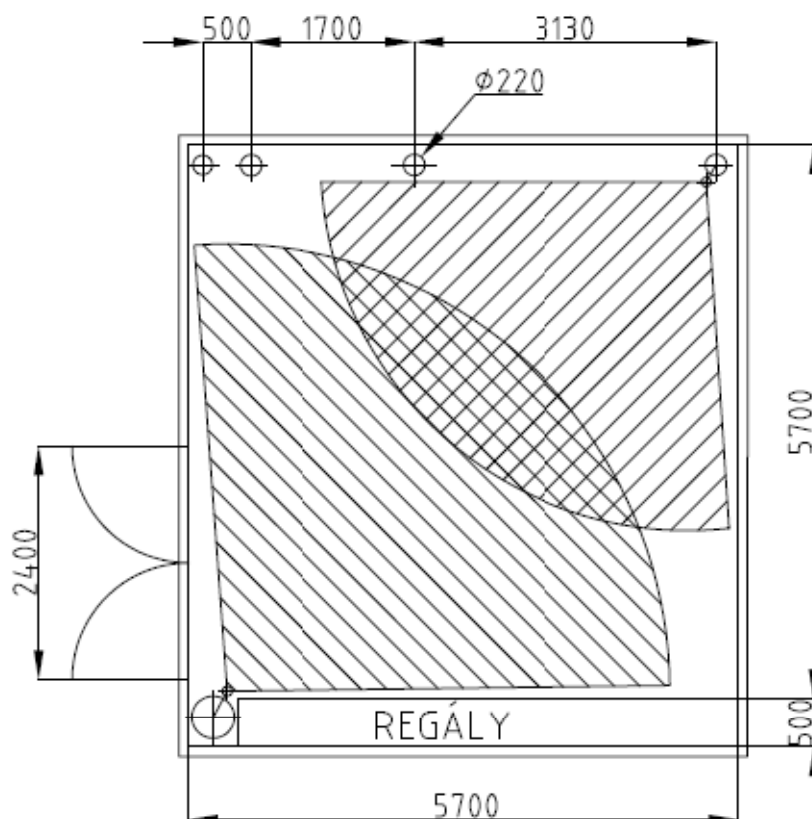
Varianta B – nová konstrukce jeřábu na nevyužitém sloupu
